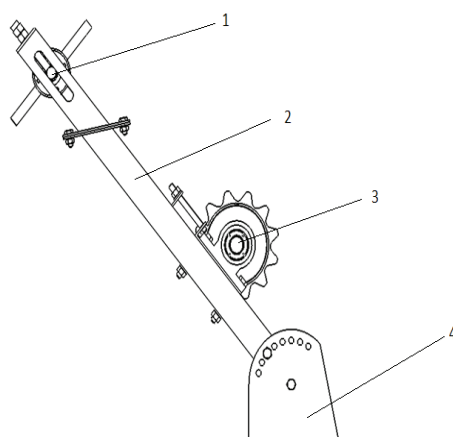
Схема устройства для регулировки угла наклона ворохоподъемного элеватора:
